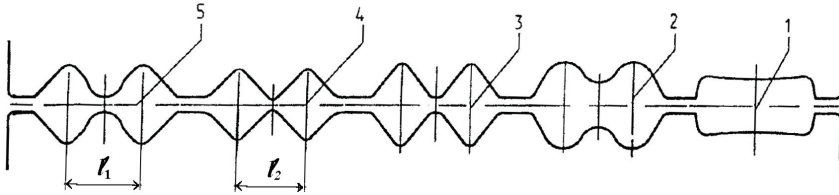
Схема калибров валков обжимного стана 850 для реализации технологии сдвоенной прокатки–разделения. 1 – ящичный калибр; 2 – первый фасонный разрезной калибр; 3 – сдвоенный ромбический калибр; 4 – сдвоенный квадратный калибр; 5 – разделительный калибр.  $l_1$  и  $l_2$  – расстояние между осями двумя ручьями сдвоенных квадратного и разделительного калибров
